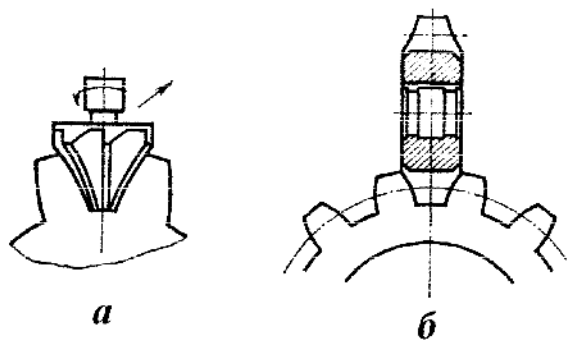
Фрезерование впадин зуба методом копирования: а - пальцевой фрезой; б - дисковой фрезой.
